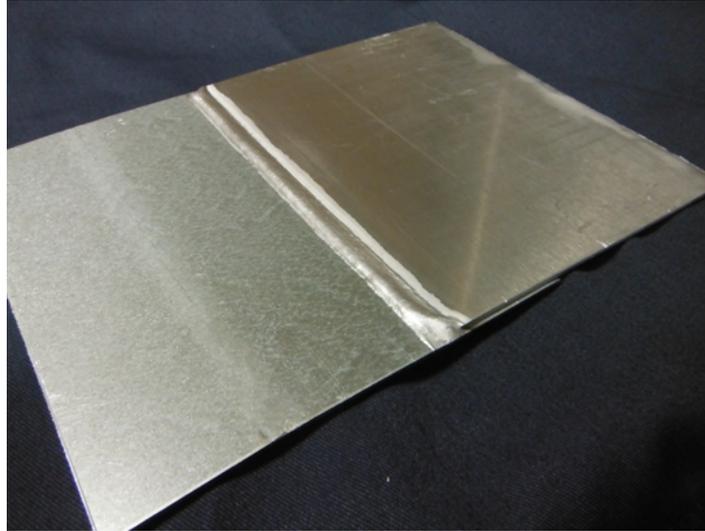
Soudage CMT aluminium sur acier galvanisé
